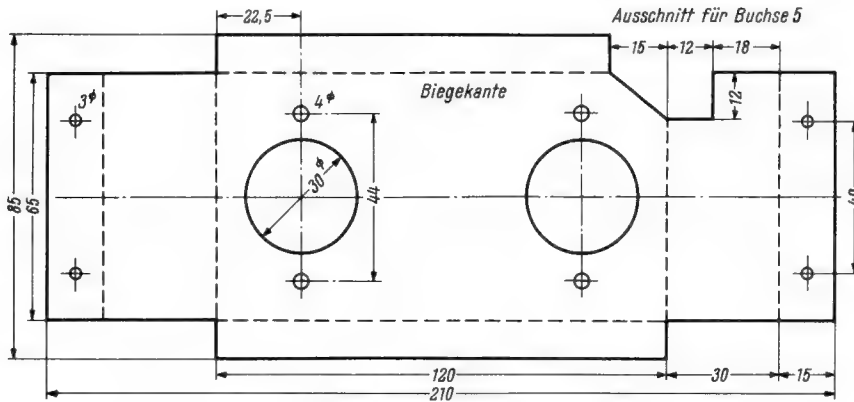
Montagewinkel für die Fassungen der Röhren RG 62 D
